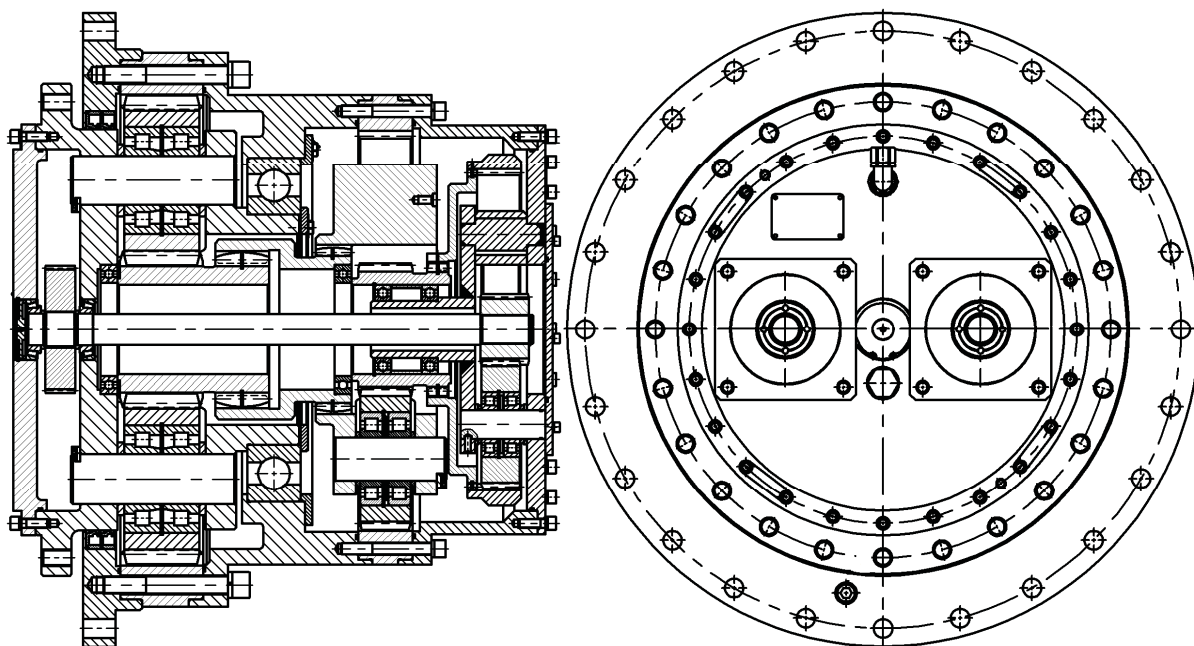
Планетарный редуктор типоразмера 2500, выполненный по схеме $(AAA)_{(b_1 b_2 h_3) a_3}^h$
